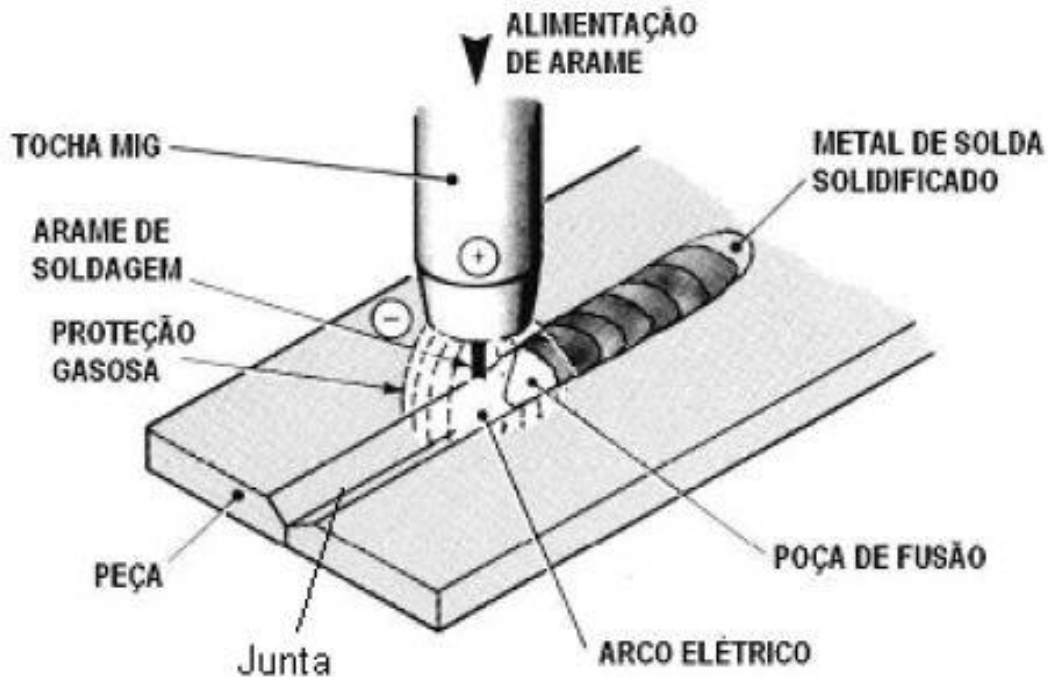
Processo de Soldagem GMAW (FORTES; VAZ, 2005)
